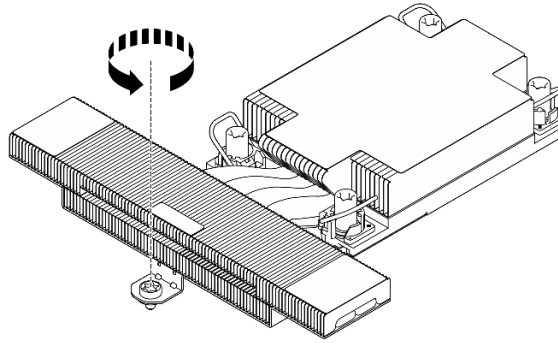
Desserrage des vis du dissipateur thermique en forme de T
